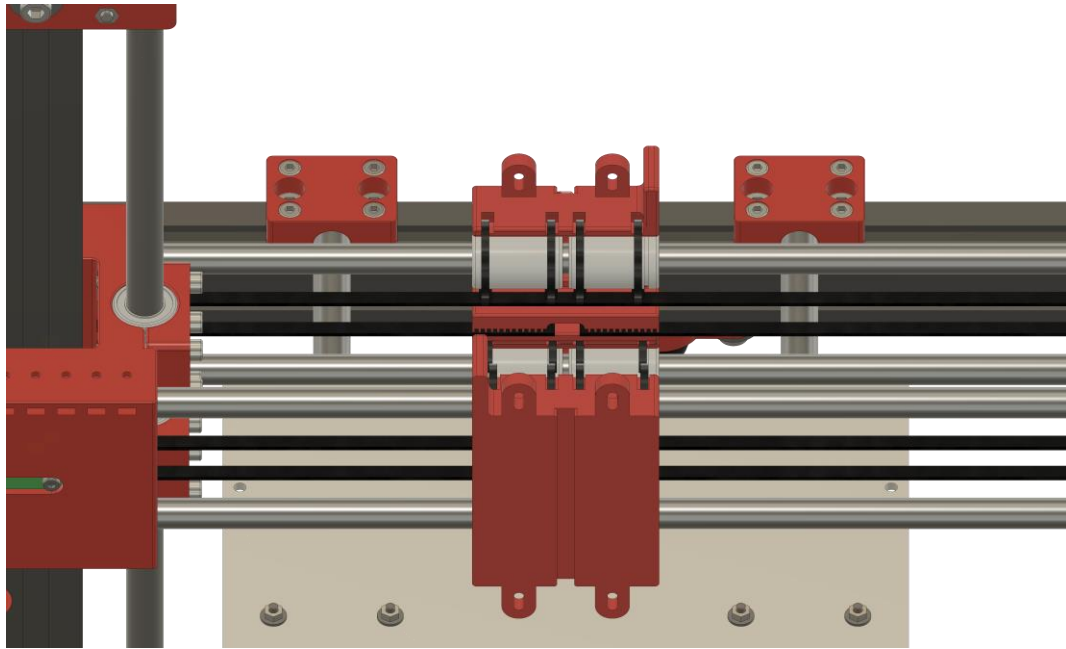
Komponenty pro sestavení krokových motorů os X
